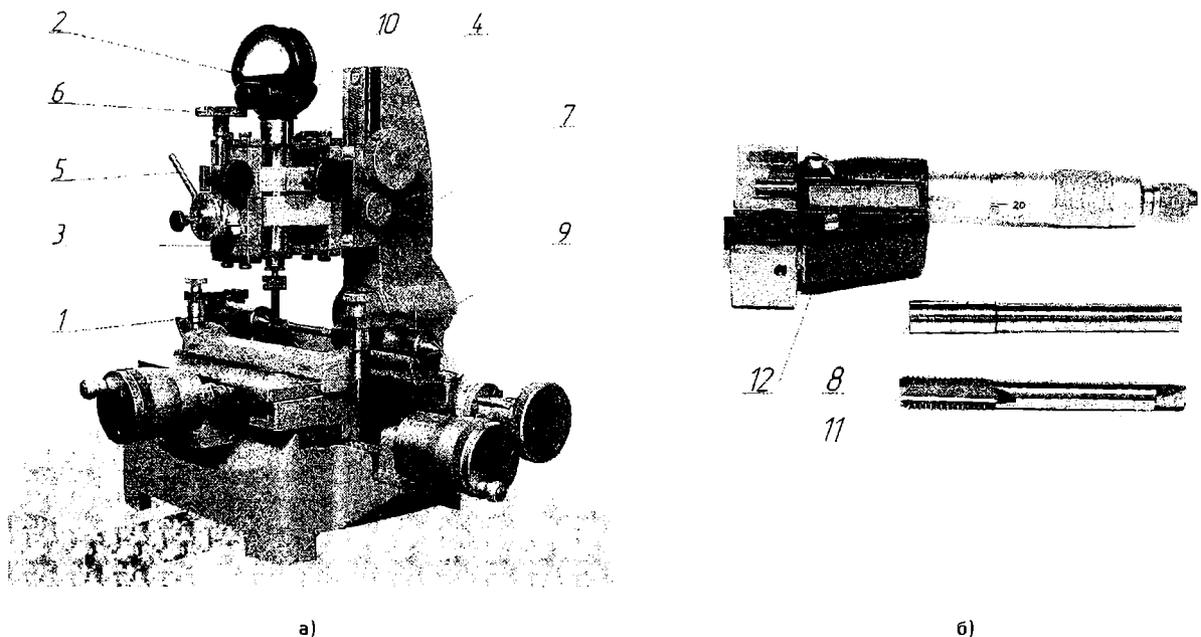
Прибор для послеоперационного измерения среднего диаметра резьбообразующего и контрольного инструмента: 1-наконечник; 2-микрокатор; 3-каретка; 4-упругая направляющая; 5-арретир; 6-винт; 7-стойка; 8-эталонная деталь; 9-центра; 10-винт настройки; 11-измеряемая деталь; 12-цифровой микрометр
